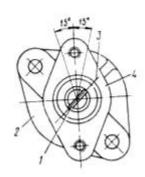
Установка зажигания 1 - указатель установки зажигания; 2 - метка на шкиве коленчатого вала
